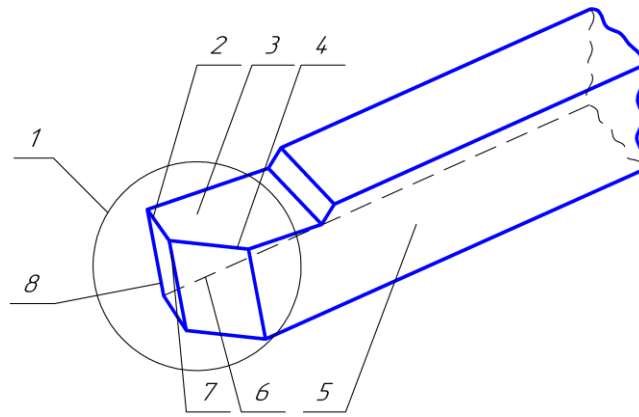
Элементы рабочей части токарного проходного резца: 1 – головка; 2 – вспомогательная режущая кромка; 3 – передняя поверхность; 4 – главная режущая кромка; 5 – державка; 6 – главная задняя поверхность; 7 – вершина резца; 8 – вспомогательная задняя поверхность
